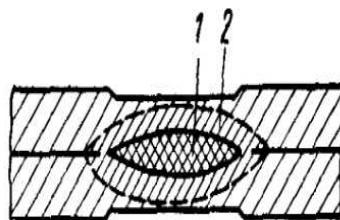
Макроструктура сварной точки: 1 – литое ядро точки;
